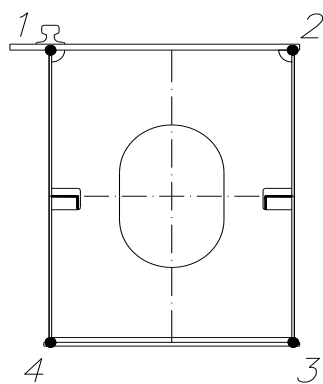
Поперечное сечение ездовой балки с характерными зонами
